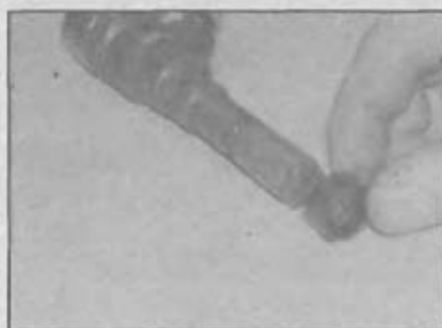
Установка нового уплотнения на корпус форсунки
